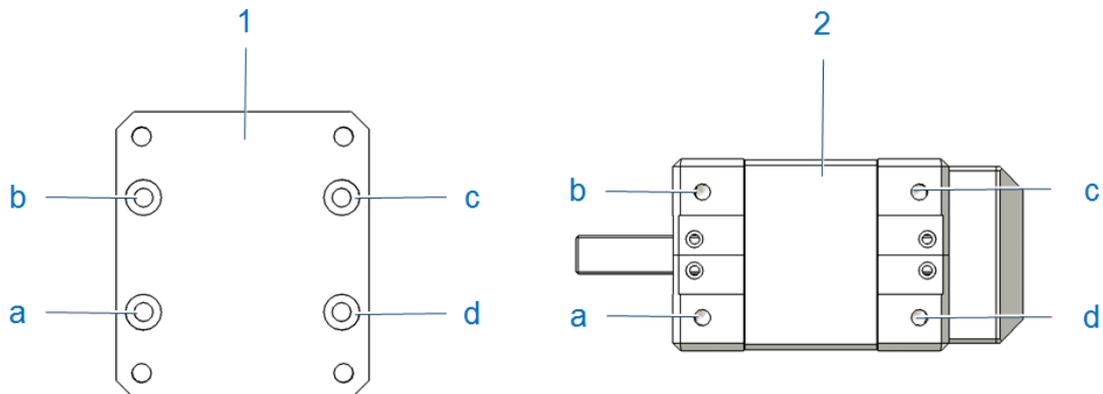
Übersicht der Montagebohrungen für Montageflansch A
